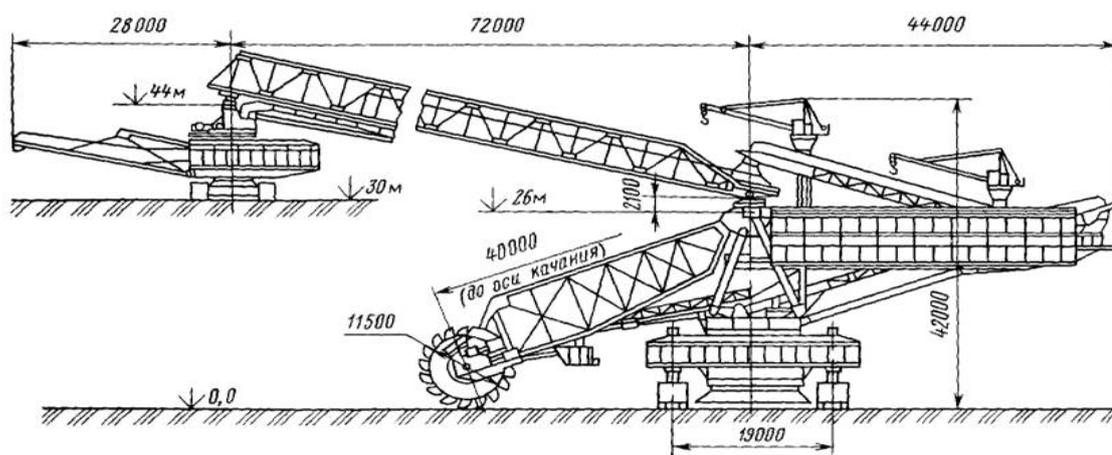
Конструктивная схема роторного экскаватора ЭРП-5250В
